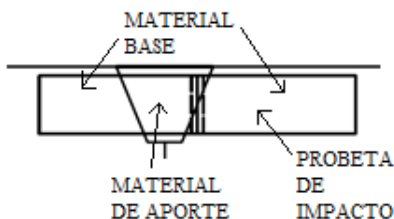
UBICACIÓN PARA LA EXTRACCIÓN DE LA PROBETA DE IMPACTO EN EL CUPON DE SOLDADURA
